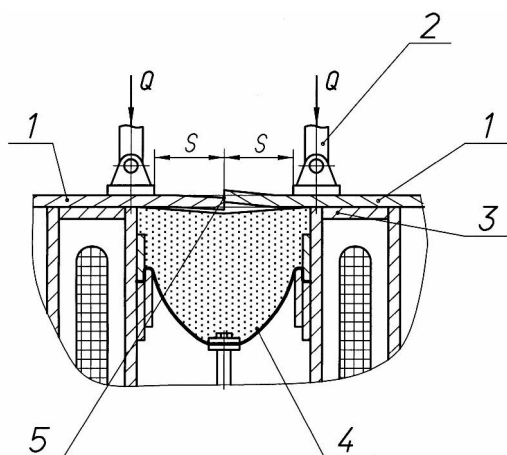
Схема сборки сварного стыка листового полотнища на стенде с механическими (пневматическими) прижимами на флюсовой подушке
